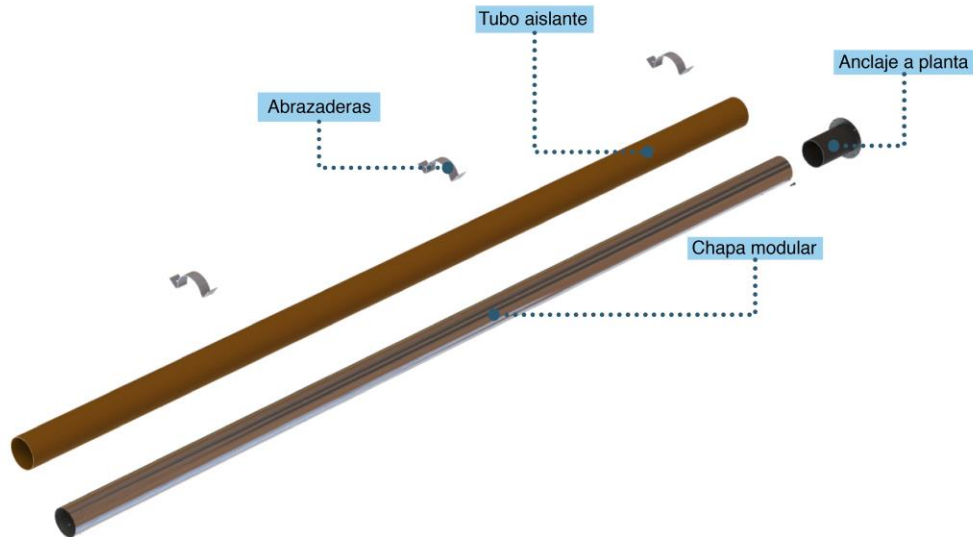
Vista explosionada conductor. Fuente: Autora.
